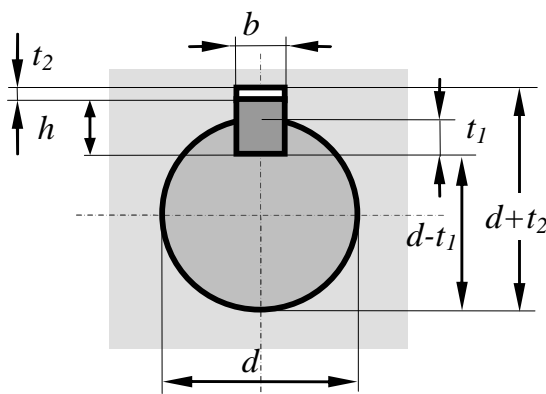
Схема розташування елементів шпонкового з'єднання
